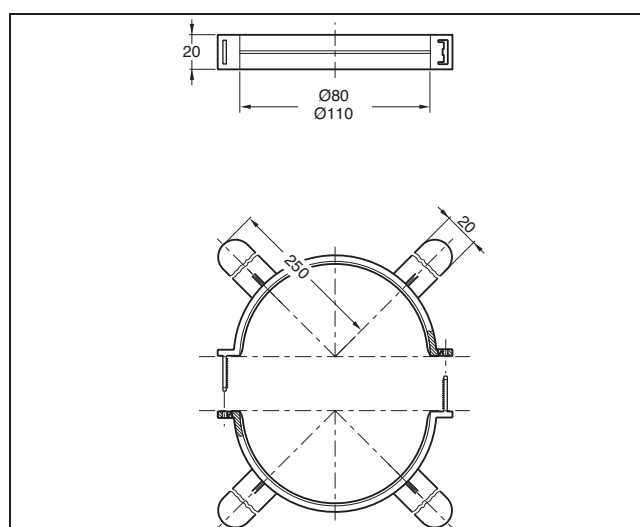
Kryt šachty pro 80 mm (rozměry v mm)
